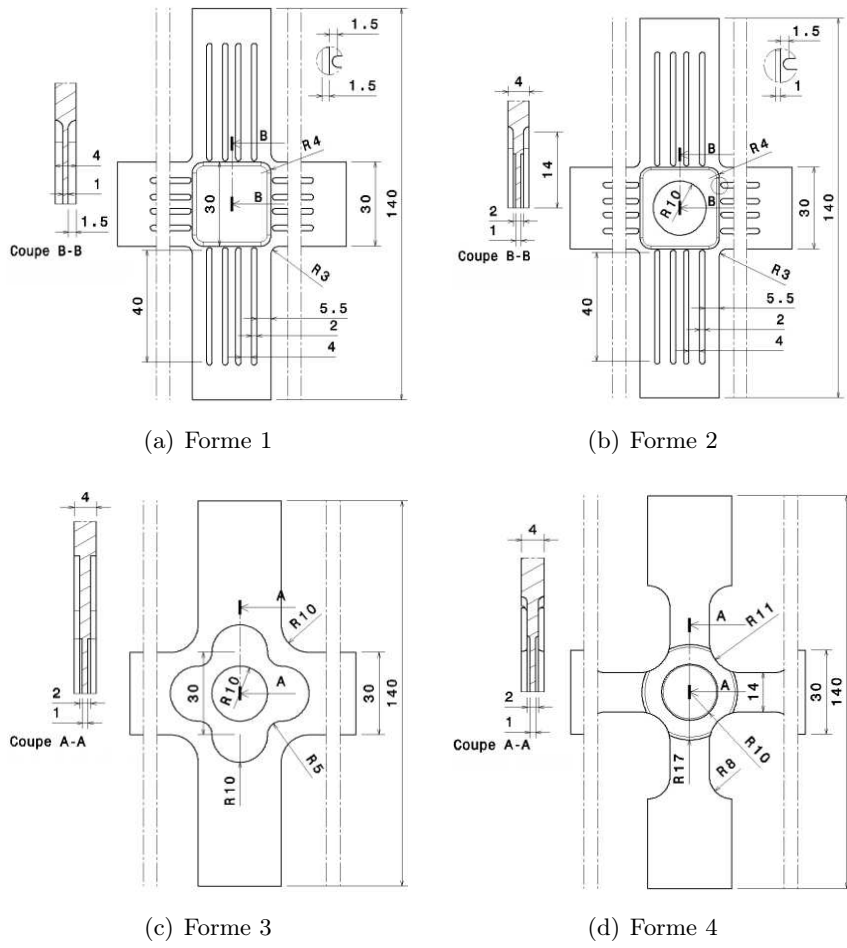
Exemples de géométries d'éprouvette cruciforme testées.
